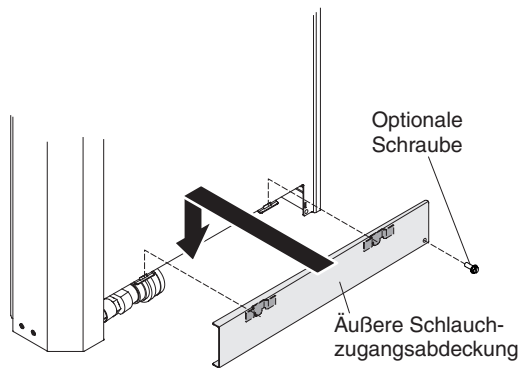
Äußere Schlauchzugangsabdeckung installieren
